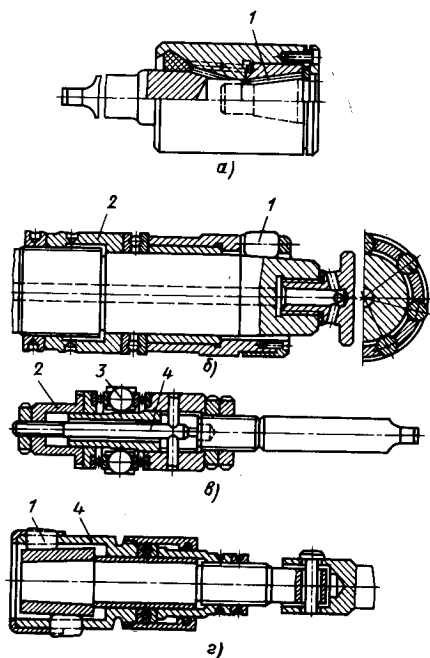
Многоэлементные инструменты для обкатывания и раскатывания: а - многороликовая обкатка для обработки хвостовика; б - жесткая роликовая раскатка для отверстий диаметром 50-150 мм; в - то же, шариковая; 2 - установочная гайка; 3 - шарики; 4 - сепаратор
